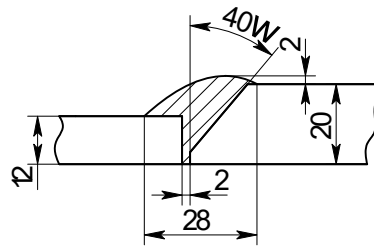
Площа наплавленого металу з'єднання С8 по ГОСТ 14771-76
